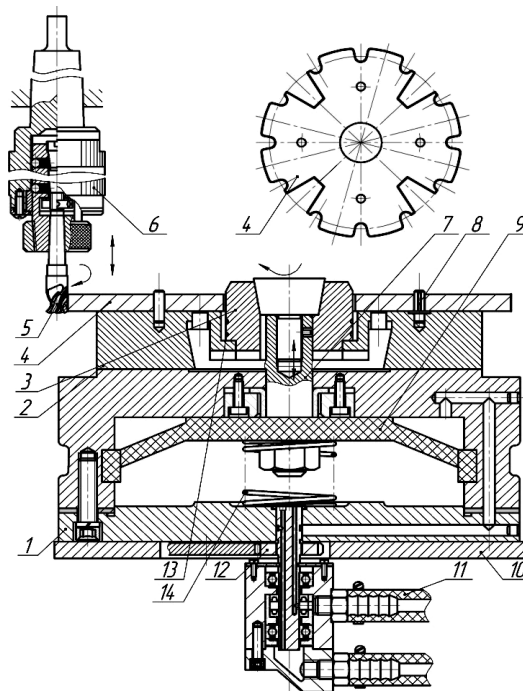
Технологічна схема виготовлення приводних зірочок шліцьових механізмів односторонньої дії оброблення привідної на верстаті з ЧПК з використанням кінцевої фрези: 1 – корпус; 2 – підставка; 3 – цанга; 4 – заготовка; 5 – кінцева фреза; 6 – затискний патрон; 7 – шток; 8 – установочні пальці; 9 – пневмокамера; 10 – стіл; 11 – шланги пневмоприводу; 12 – приводні зірочки; 13 – пружина стиснення; 14 – пружина пневмоприводу
